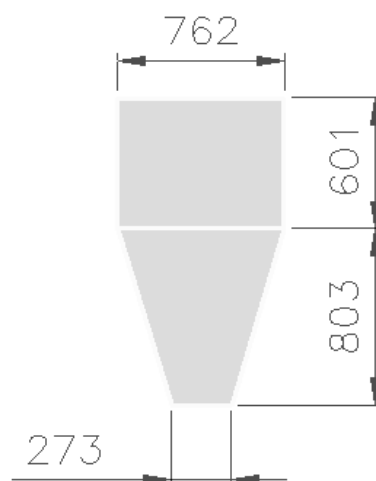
DIMENSIONES DE LA TOLVA (MM)
